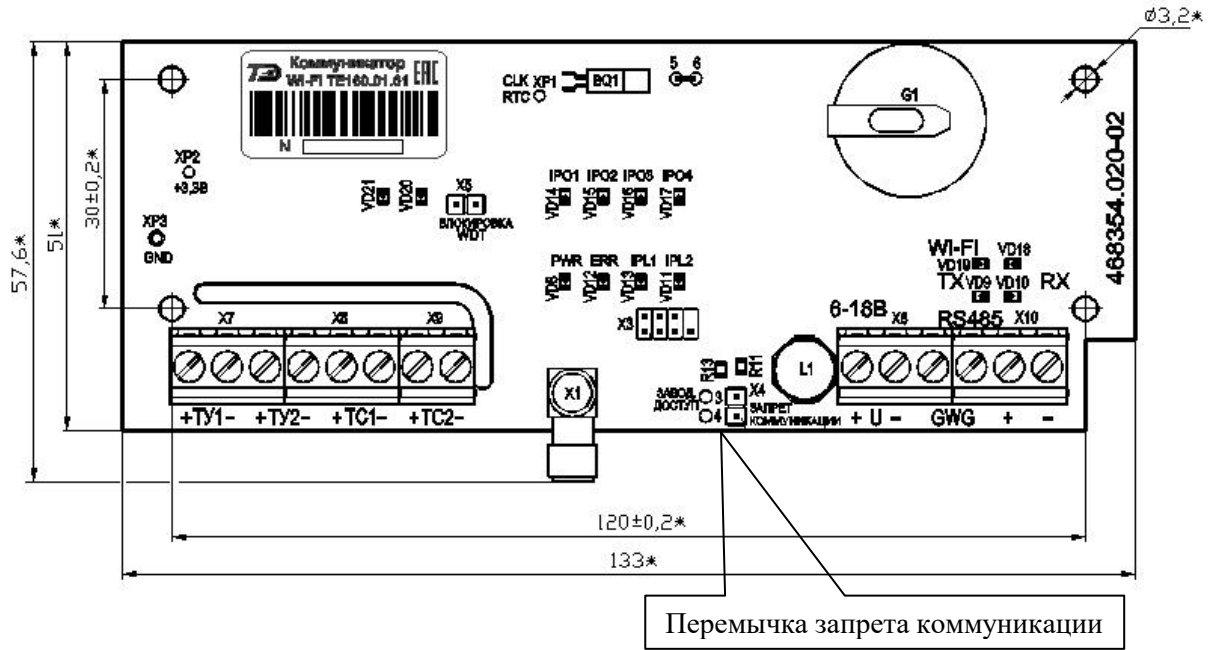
Габаритный чертеж и установочные размеры коммуникатора Wi-Fi TE160.01.01
